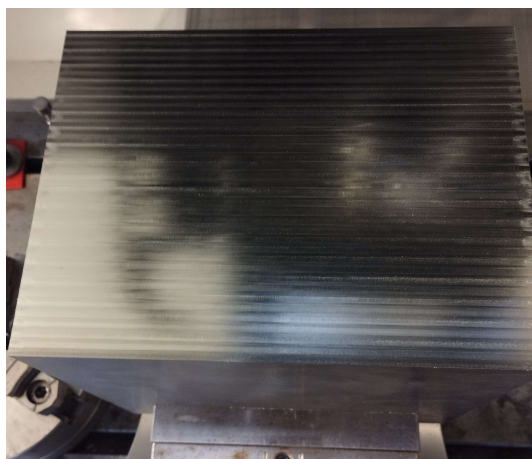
Bloco de aço W 1.2711 utilizado nos testes de maquinagem.
